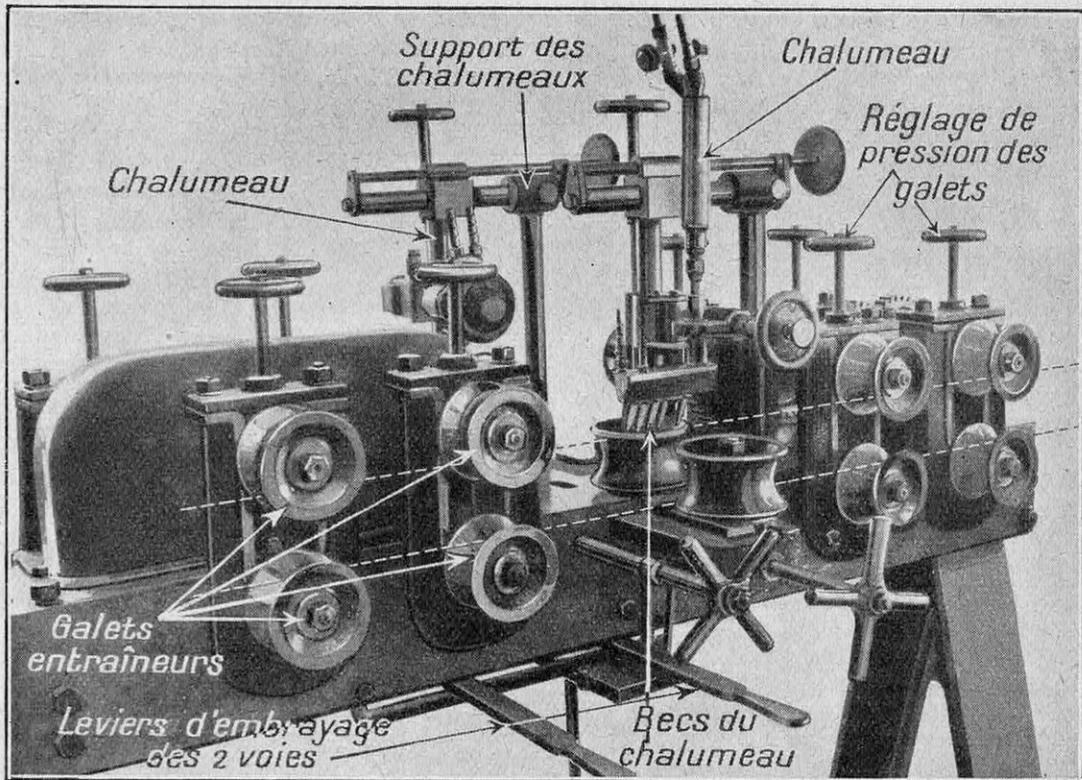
MACHINE A SOUDER LES TUBES, A DEUX VOIES, DE LA « S. A. F. »
